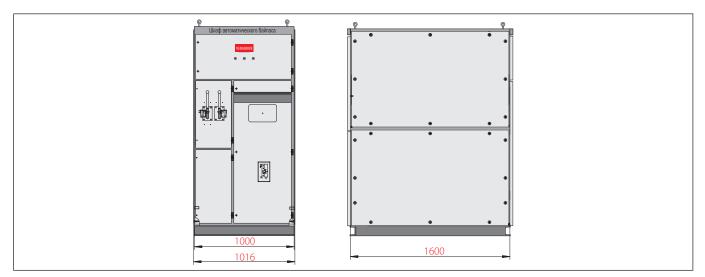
Корпус шкафа автоматического байпаса типоразмера АВО2
